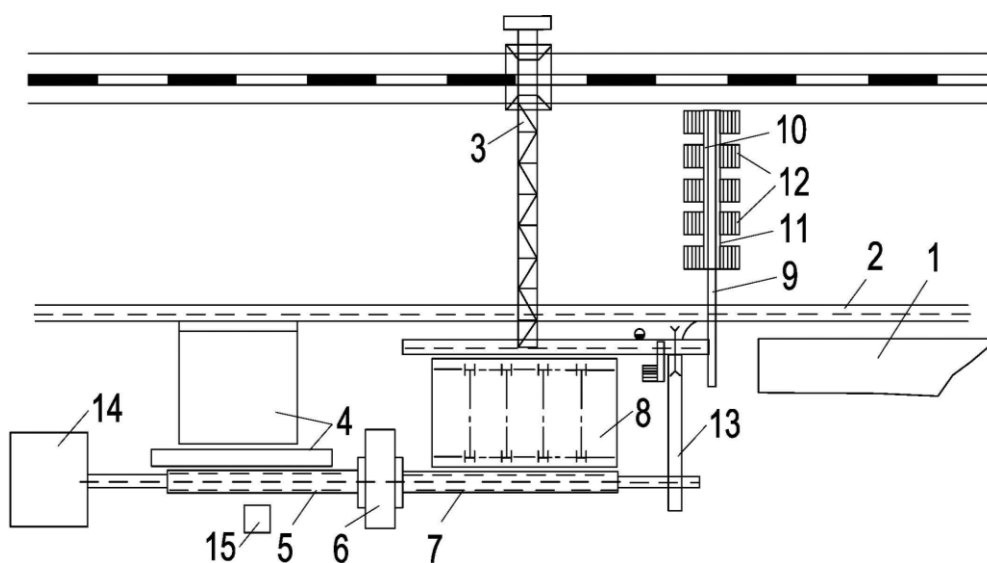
Схема поточной линии экспортных балансов Вивинского леспромхоза [22]: 1 – площадка раскряжевочная; 2 – транспортер сортировочный; 3 – кран башенный; 4 – магазин буферный М-10 с торцевывравнивателем; 5 – подающий транспортер окорочного станка; 6 – станок окорочный ОК-3; 7 – приемный транспортер окорочного станка; 8 – цепной поперечный транспортер; 9 – транспортер выносной; 10, 11 – площадки сортировочные; 12 – карманы-накопители; 13 – транспортер отходов; 14 – бункер отходов; 15 – кабина оператора
